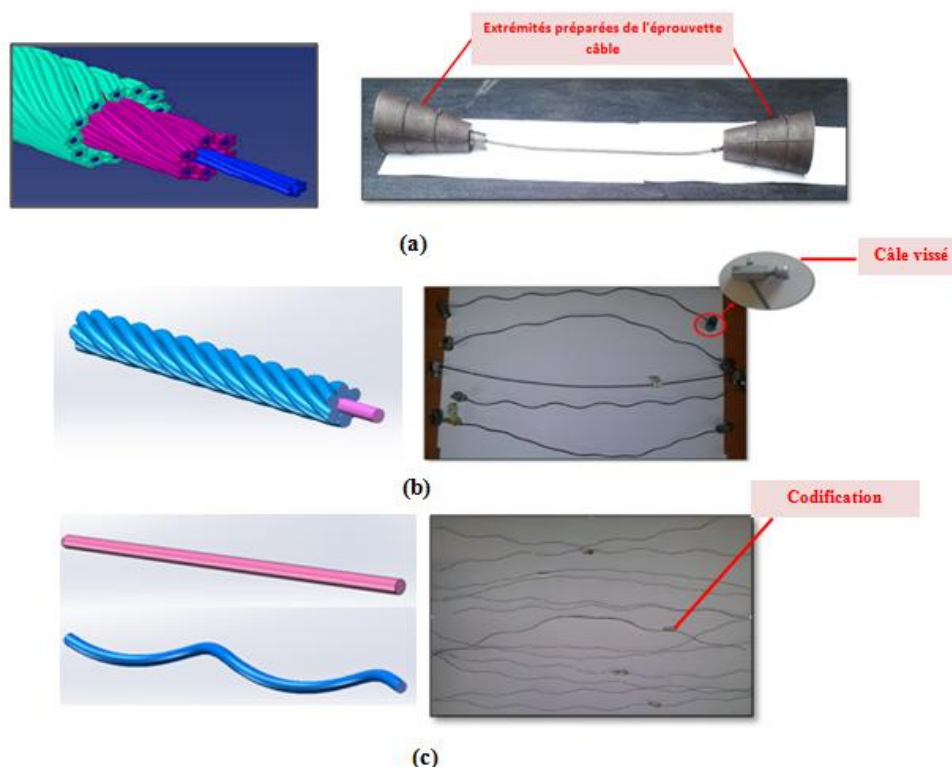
Dimensions des éprouvettes a) câble b) toron et c) fils
